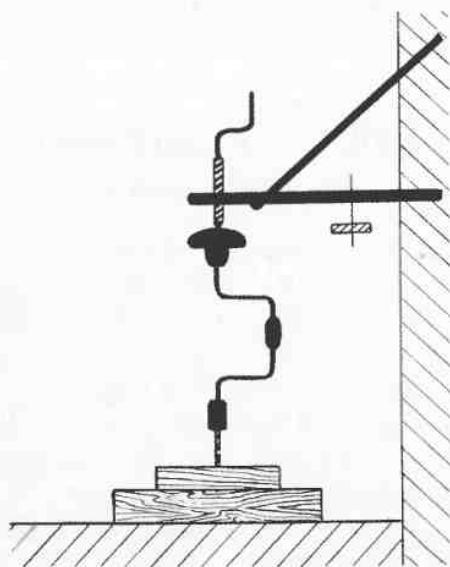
Фиксирующее приспособление для сверления в металле и дереве отверстий коловоротом с контрпором с помощью винта и ручки
